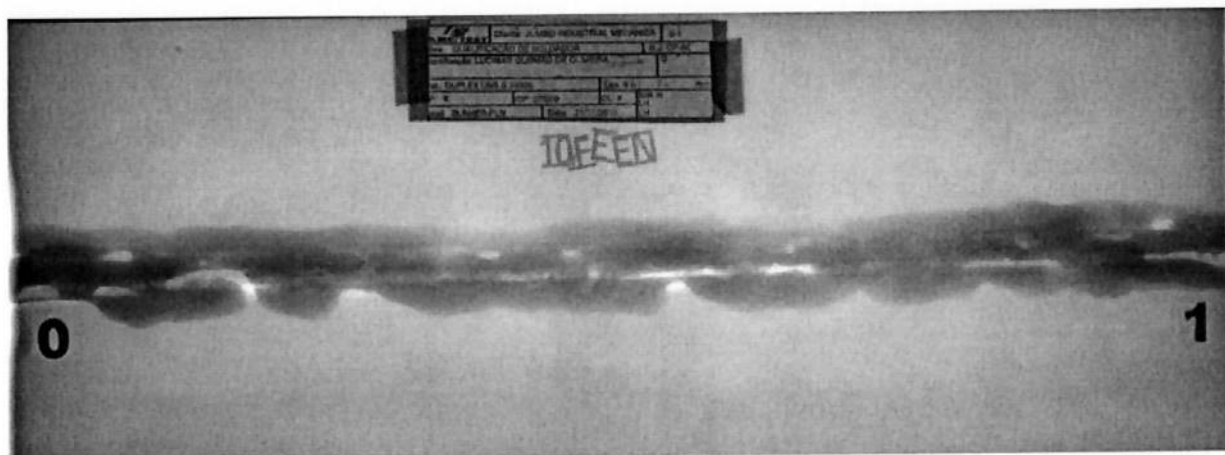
Ensaio por Raios-X na soldagem na junta soldada com 100% Argônio.
